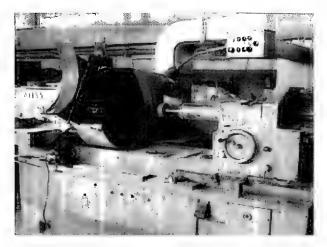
Общий вид токарно-лобового станка модели РТ-103
